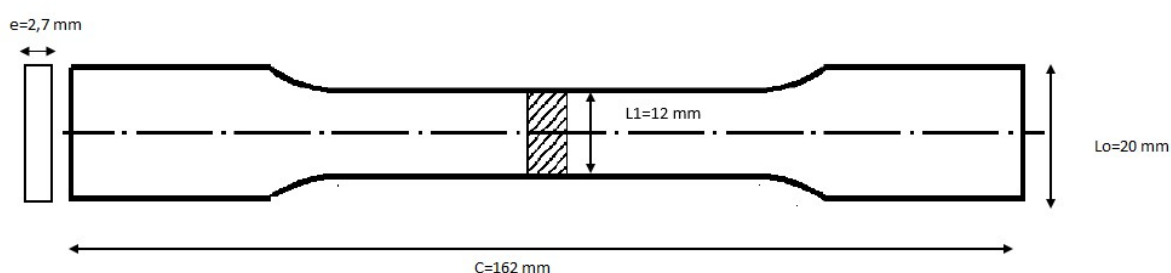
Ilustração do corpo de prova obtido da moldagem por injeção.
